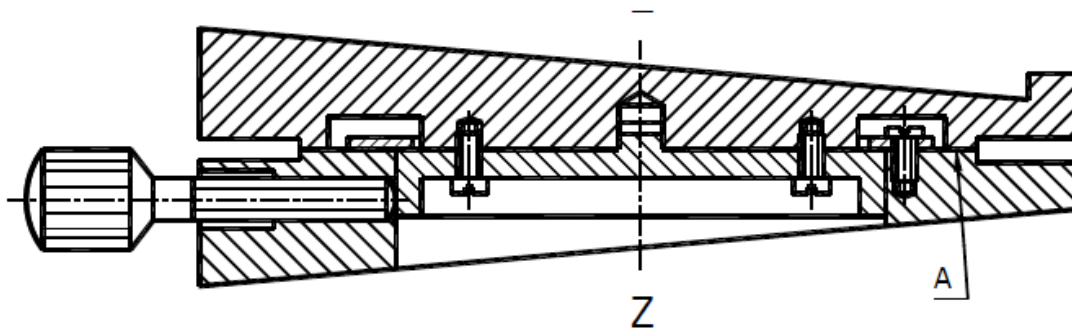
Направляючі ковзання для обертювих деталей
